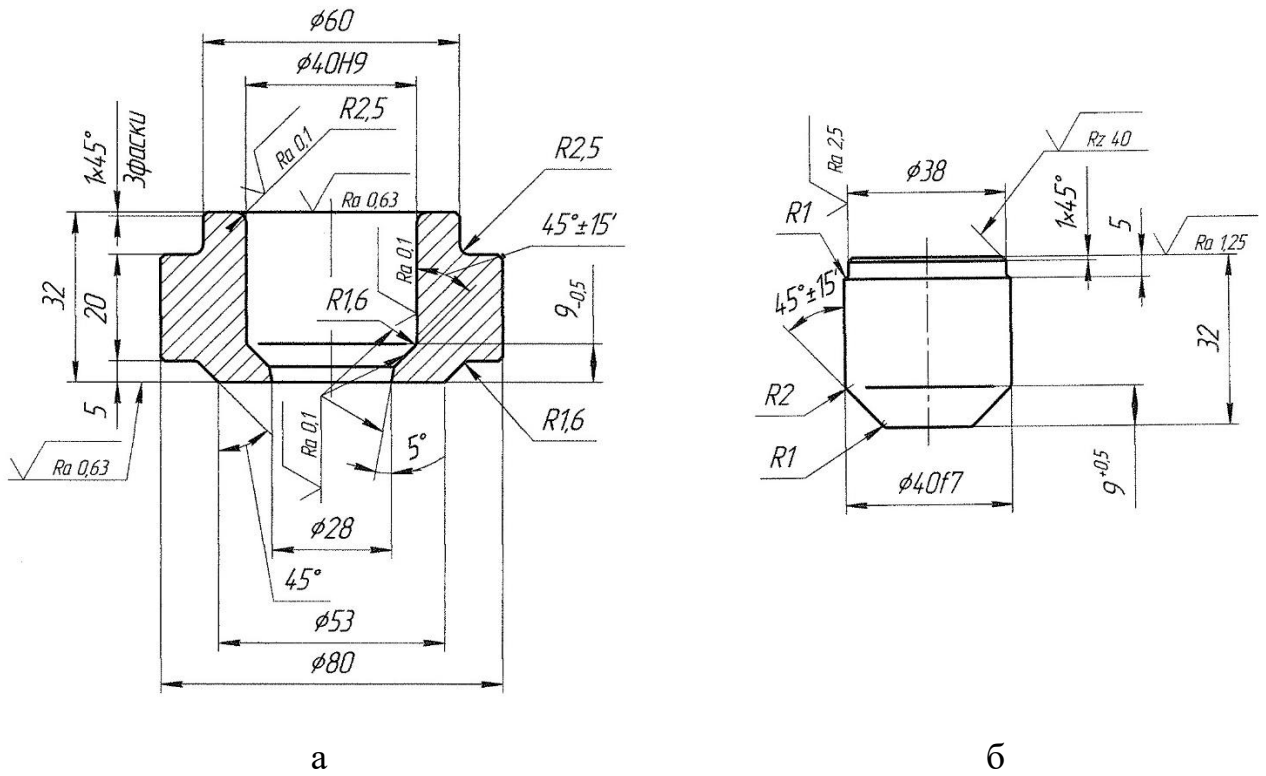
Загрузочная камера для литейного прессования:
